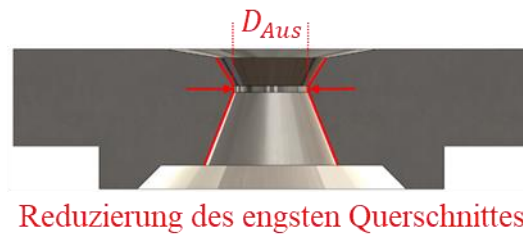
Reduzierung des engsten Querschnittes der Düsenplatte
